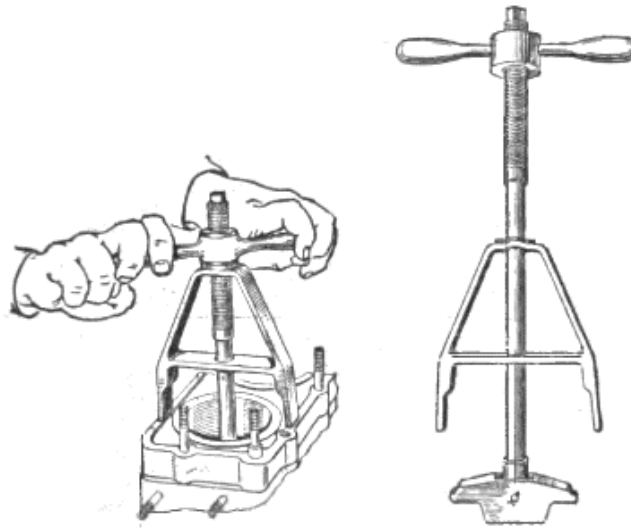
Приспособлення для витягування гільзи циліндрів
